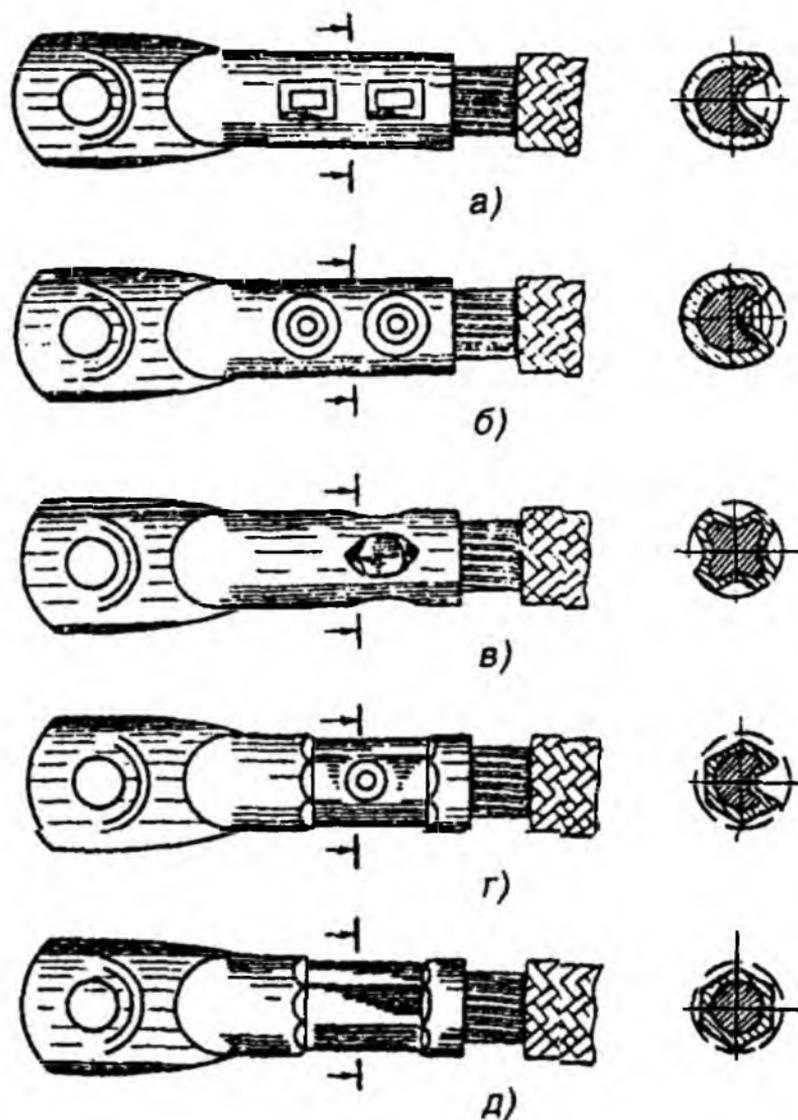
Общий вид контактных соединений, выполненных различными способами опрессовки:
